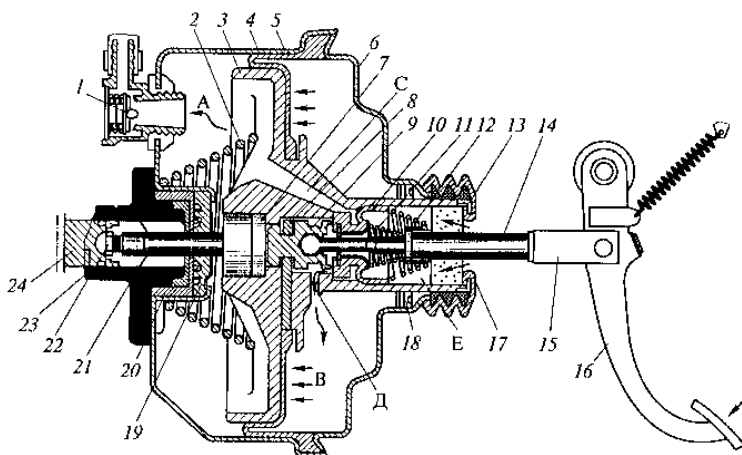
Вакуумный усилитель тормозного привода автомобилей
